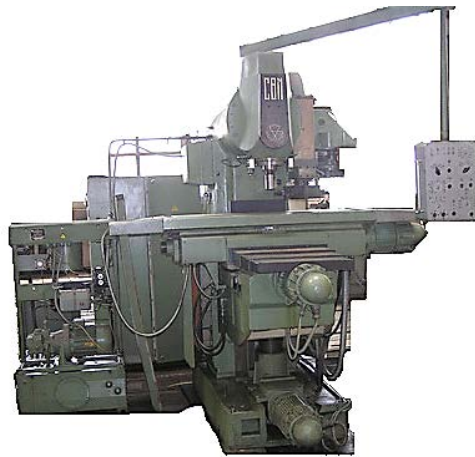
Вертикальний багатоцільовий верстат мод. СВМ1-Ф4 з ЧПК.
